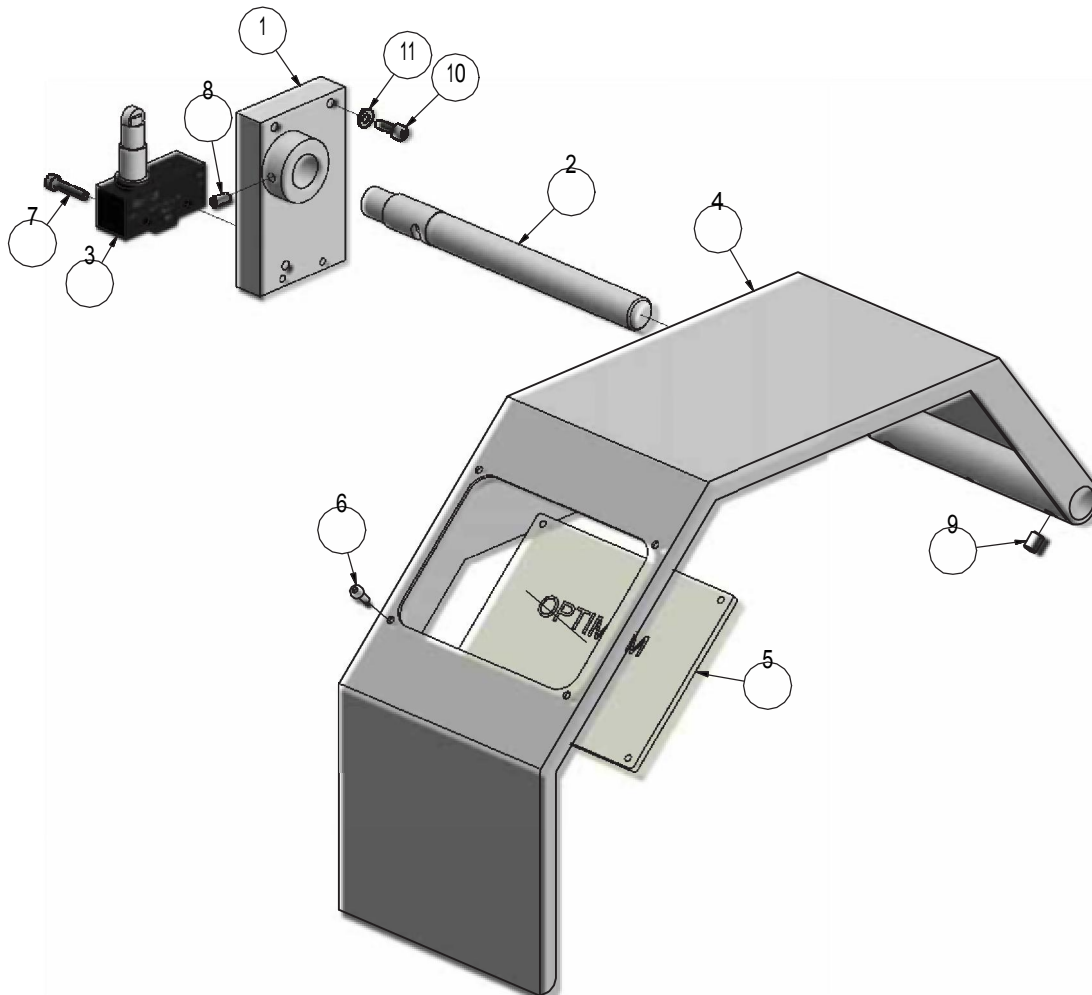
Drehfutterschutz - Lathe chuck cover
